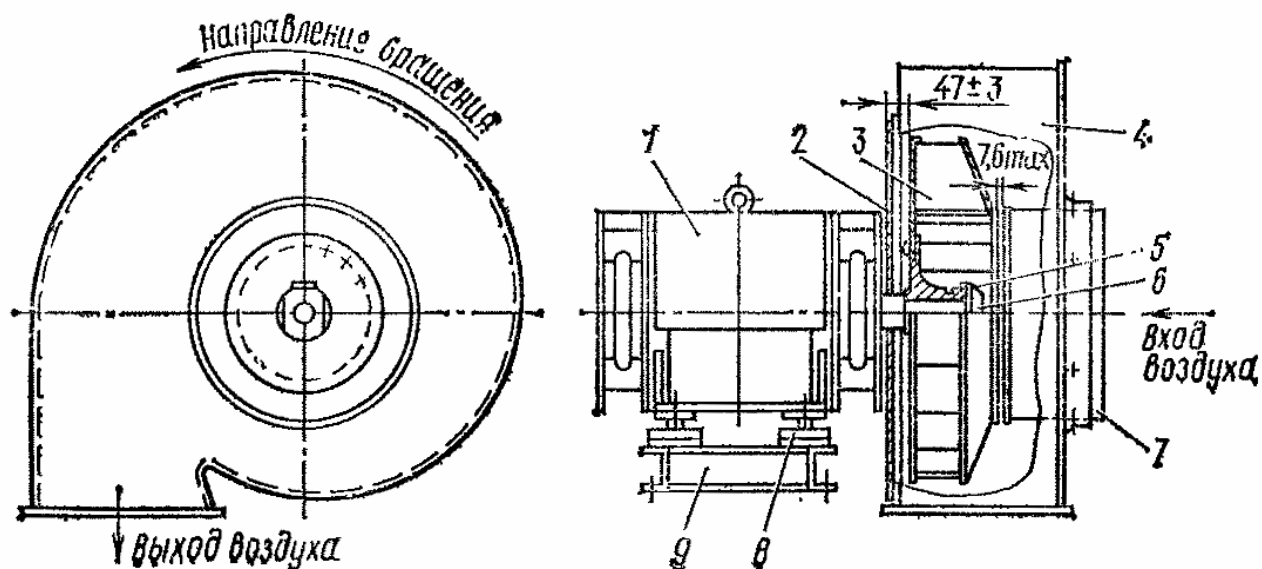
Блок центробежного вентилятора Ц8-19 № 7,6
